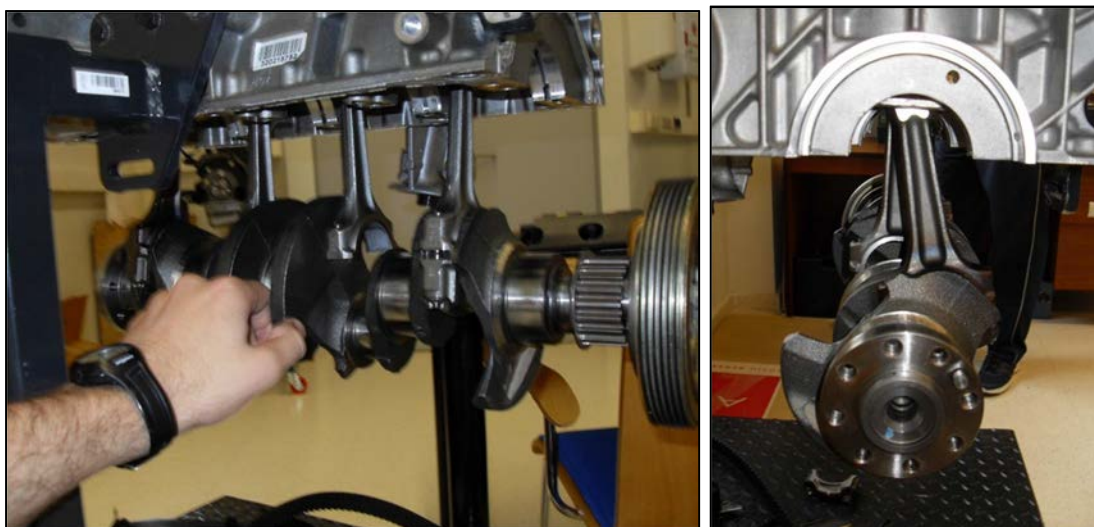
y 53. Proceso de selección de la pieza del motor que deberemos quitar para proceder posteriormente a realizar el ejercicio de dibujo. Fuente: Archivo particular.
